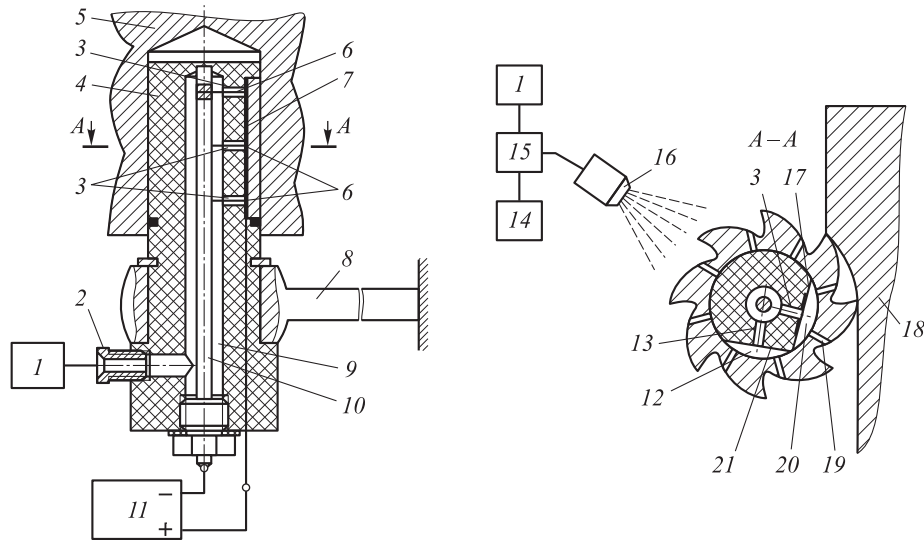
Схема устройства для охлаждения зоны резания фрезерного станка:
